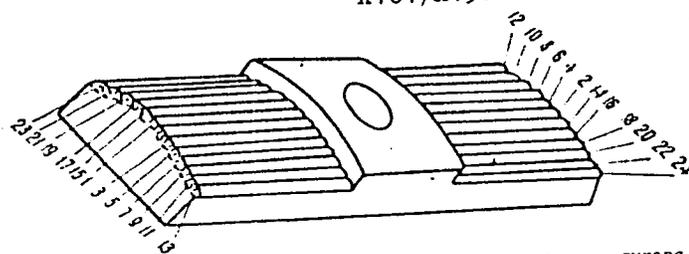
Порядок наплавки валков на цилиндрическую часть сухаря.
